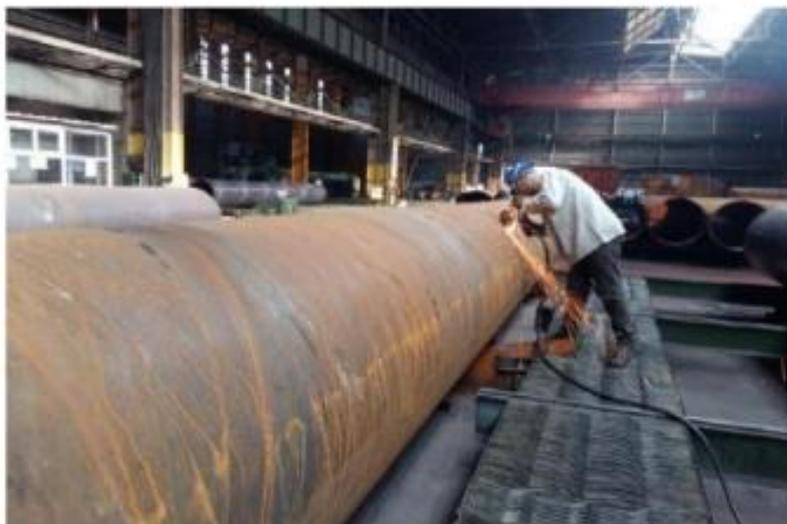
Zone de réparation manuelle du défaut de soudage [5].
